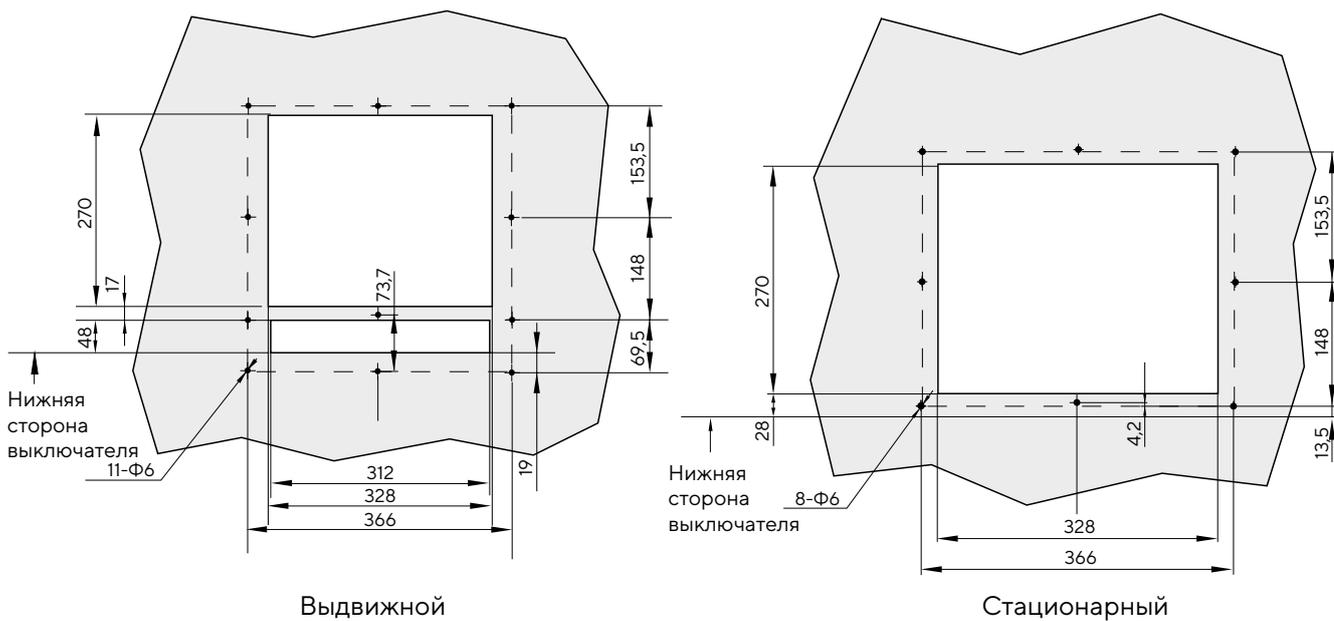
Габаритные размеры рамки обрамления выреза в двери для выключателей типоразмера Е
